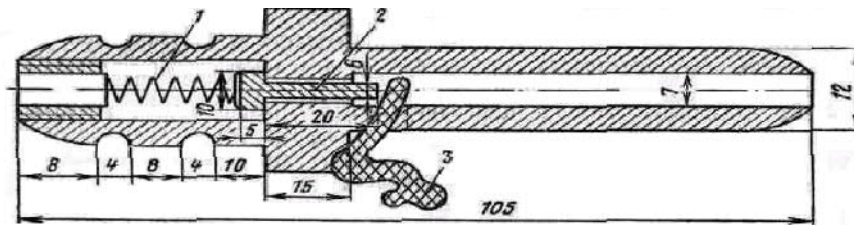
Форсунка для обдувки приборов сжатым воздухом
